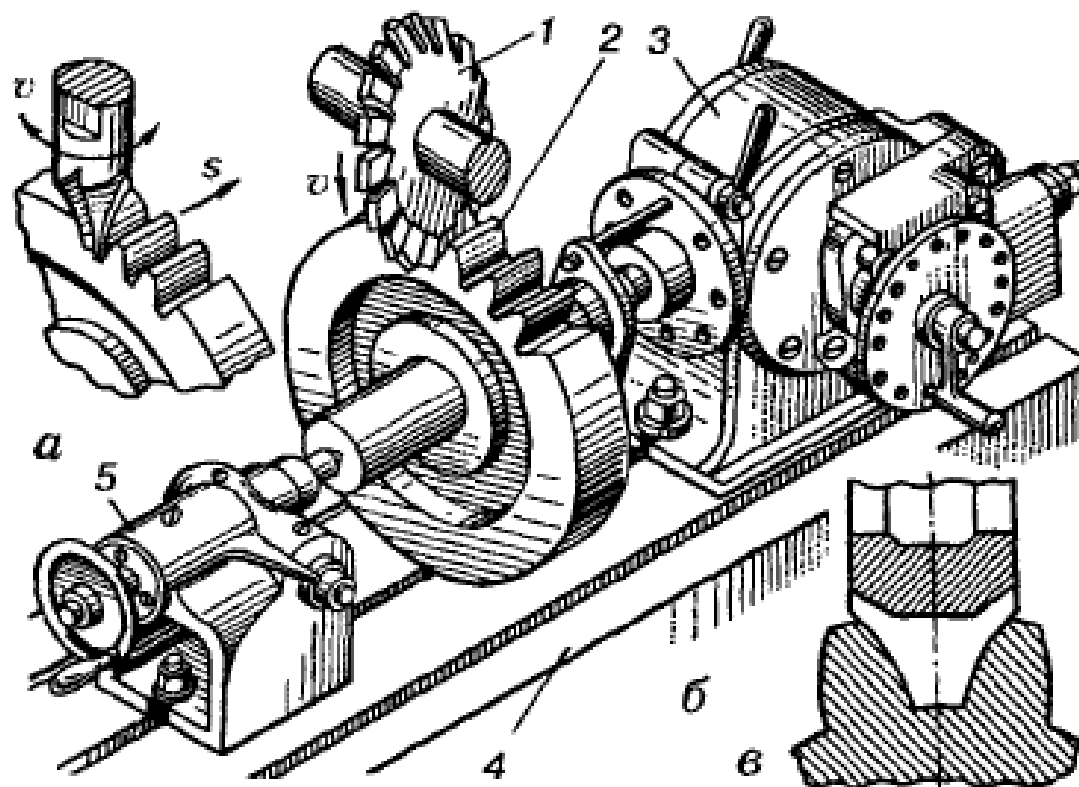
Фрезерування зубців зубчастих коліс методом копіювання
